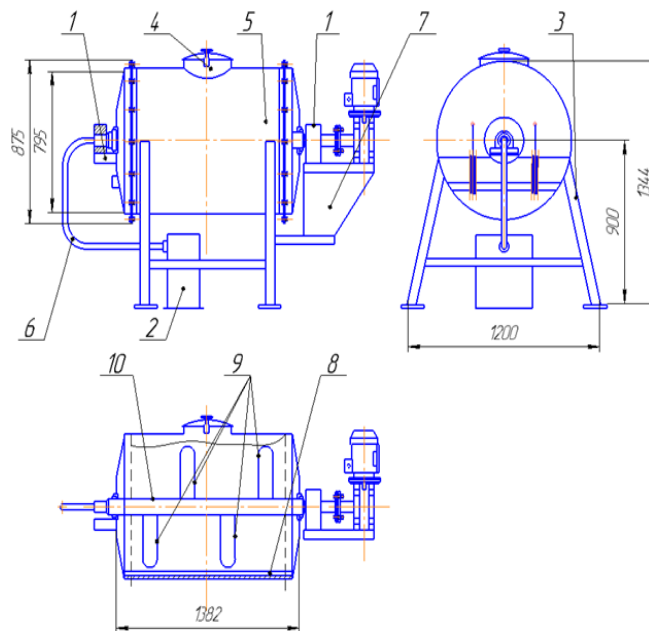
Схема установки для масування м'яса в масажері: 1 – опора; 2 – вакуумний насос; 3 – рама; 4 – кришка; 5 – циліндричний барабан; 6 – трубопровід; 7 – корпус приводного механізму; 8 – пластина; 9 – циліндричні лопаті; 10 – вал.
